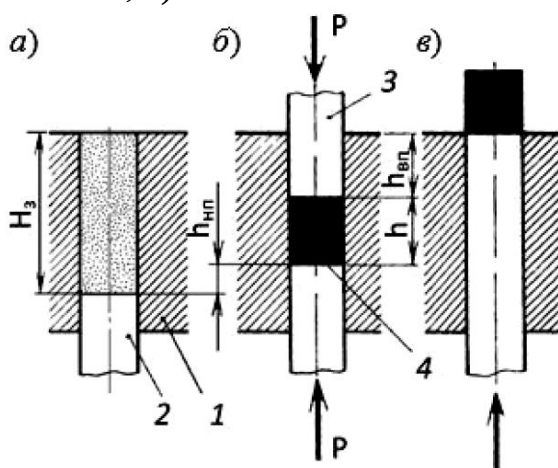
Схема пресс-формы с неподвижной матрицей для двустороннего прессования: а – заполнение матрицы порошком; б – прессование; в – выталкивание заготовки: 1 – матрица; 2 – пуансоны; 3 – заготовка
